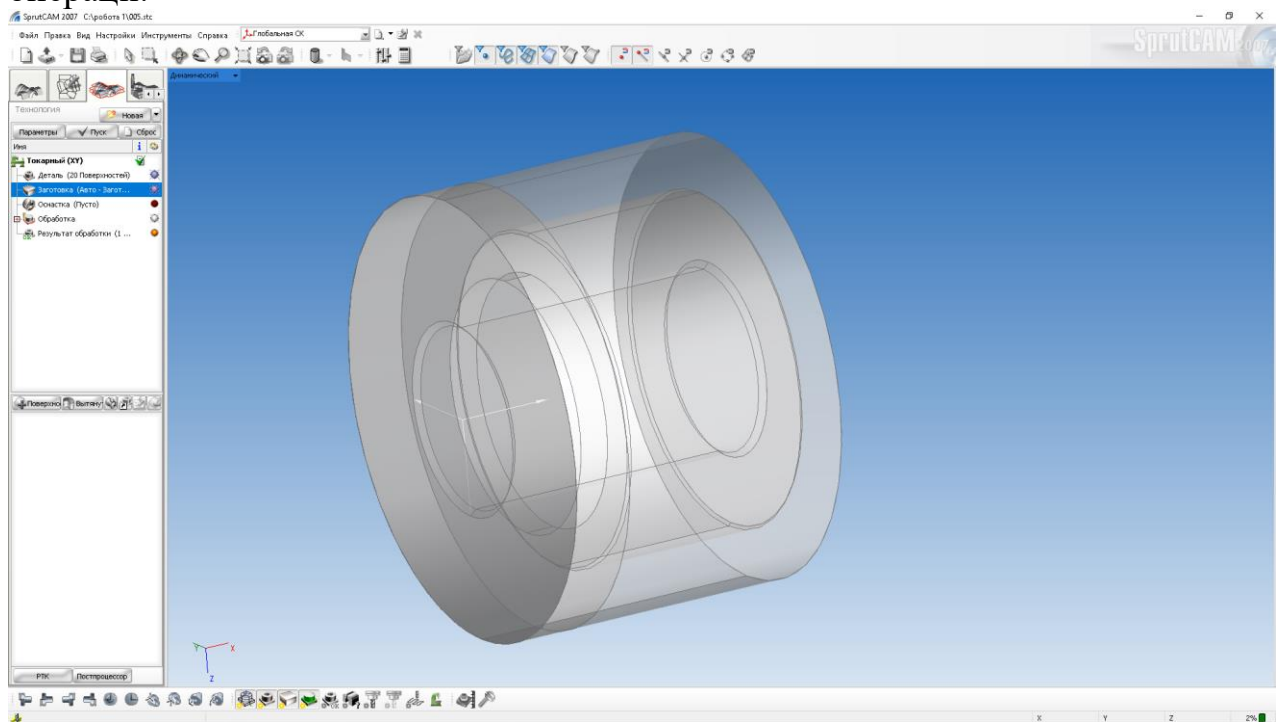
3D-моделі заготовки та деталі, імпортовані у систему SprutCAM
